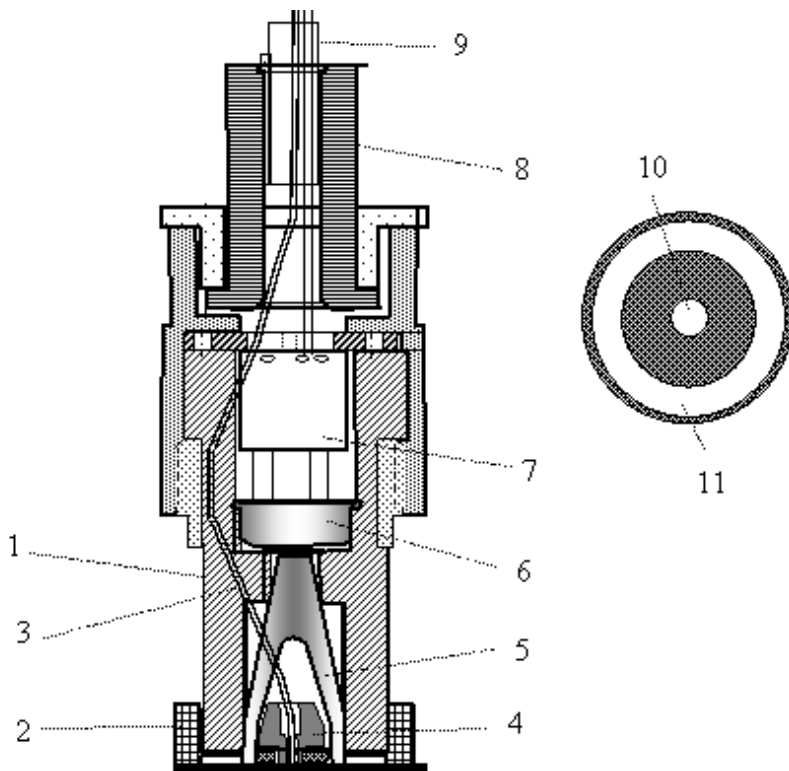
Конструкция выносной оптоэлектронной головки сенсора гемоглобина: 1 – корпус головки; 2 – насадка-диафрагма; 3 – оптическое волокно; 4 – фиксатор облучателя; 5 – конусообразный оптический фокон; 6 – фотоприемник; 7 – предварительный усилитель фототока; 8 – фиксатор соединительного кабеля; 9 – кабель
